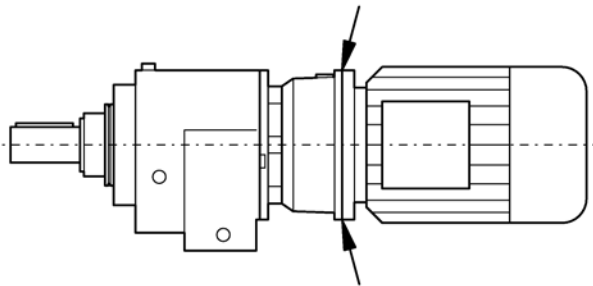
Abzudichtende Fläche beim Anbau eines IEC Motors
